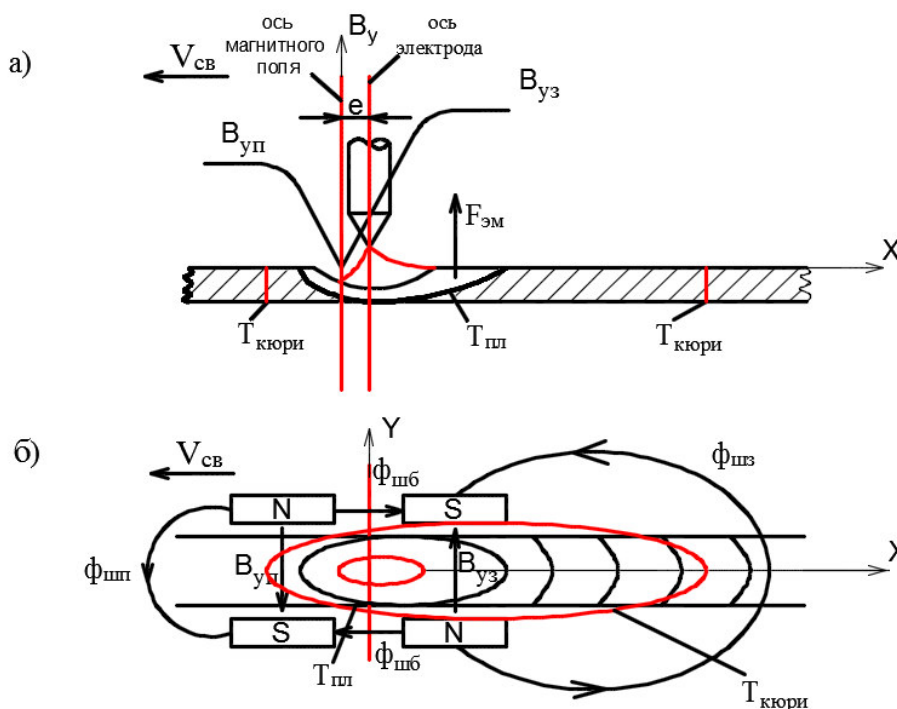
Дуга в квадрупольном магнитном поле при сварке ферромагнитных металлов при удержании сварочной ванны:
